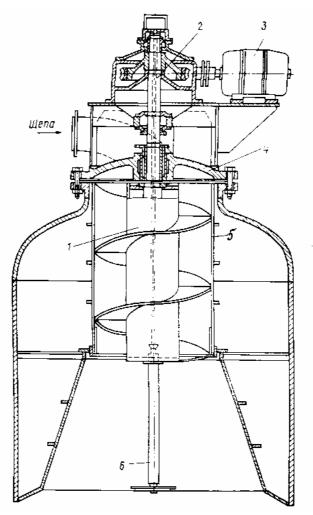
Верхняя горловина варочного котла: 1 - загрузочный шнек; 2 - вал; 3 - электродвигатель; 4 - крышка; 5 - сетчатый цилиндр; 6 - штанга
